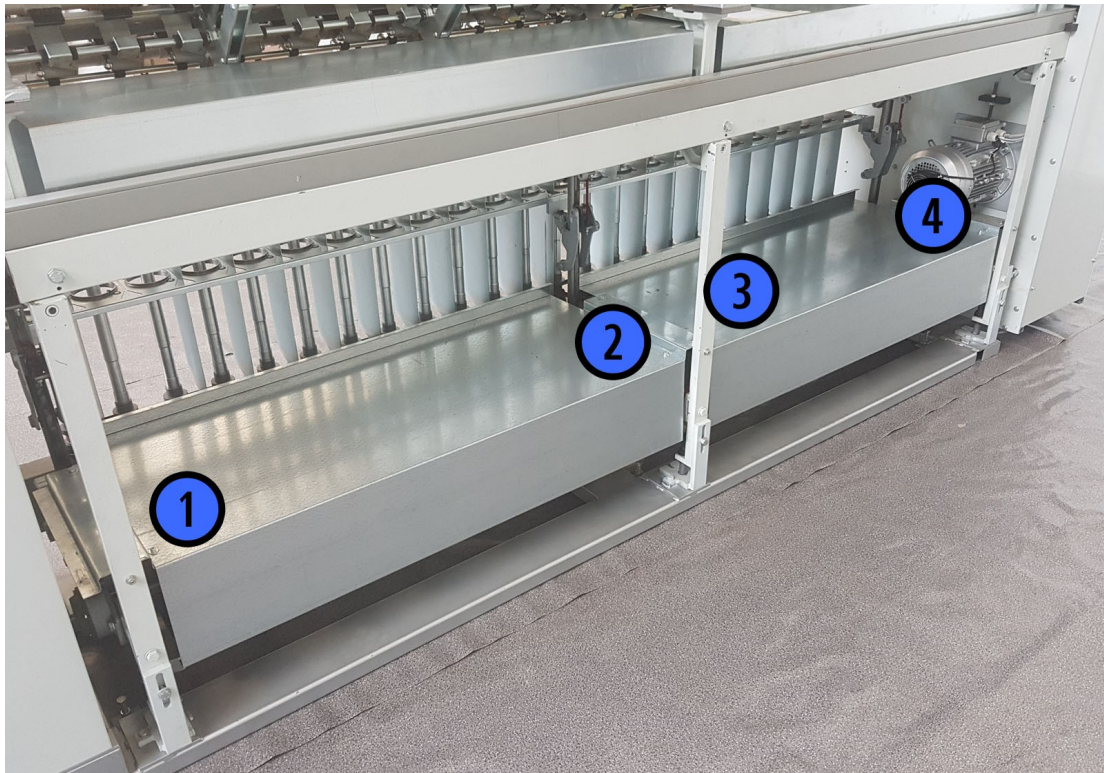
Rimozione delle lamiere di protezione posteriore
